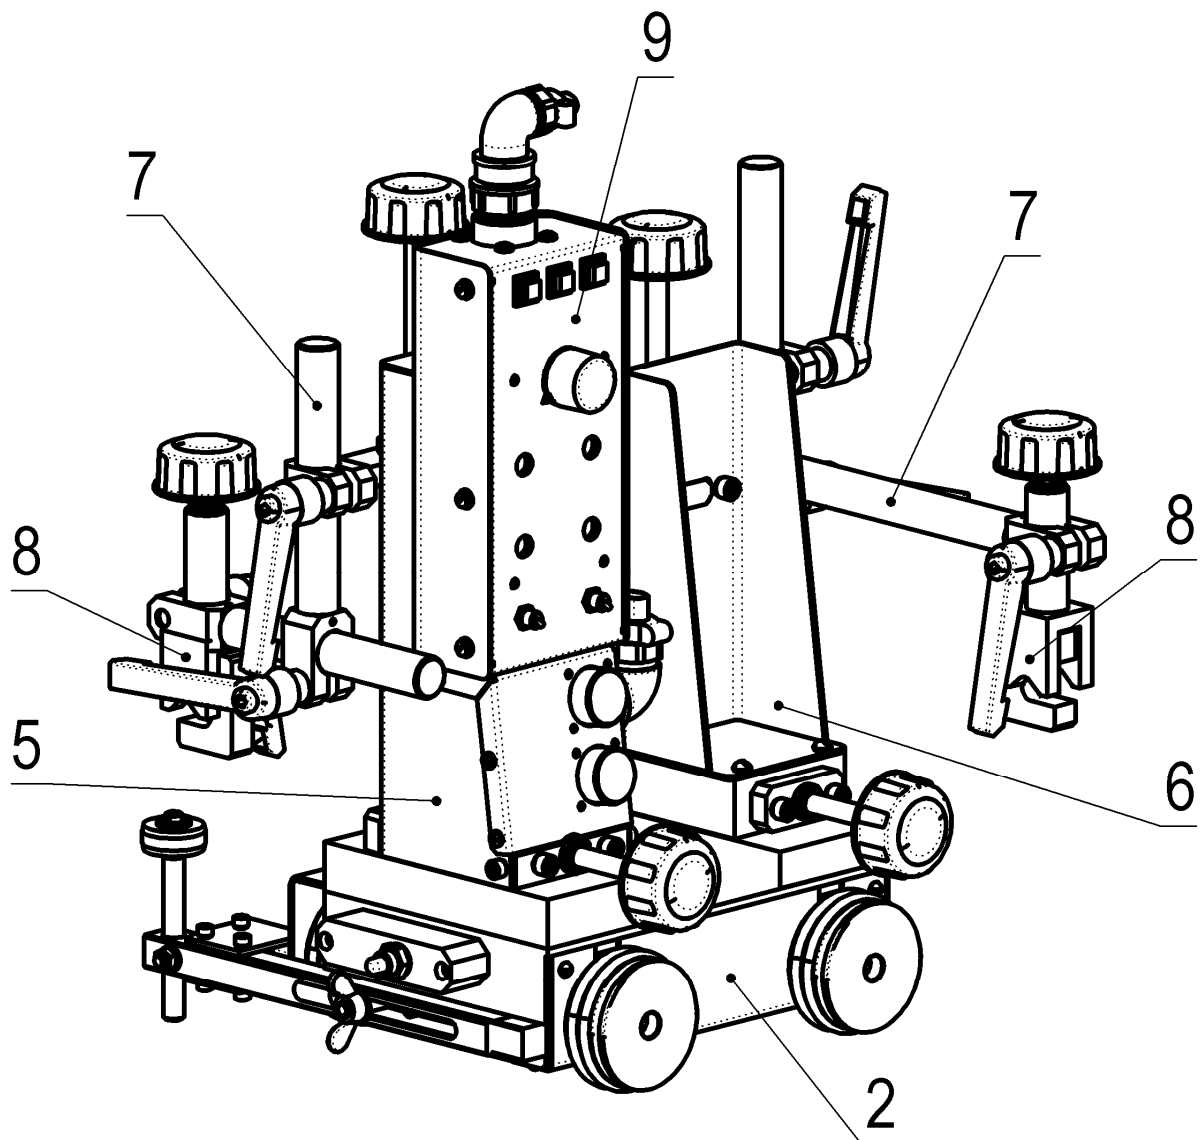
Трактор сварочный АДГ-500-1
